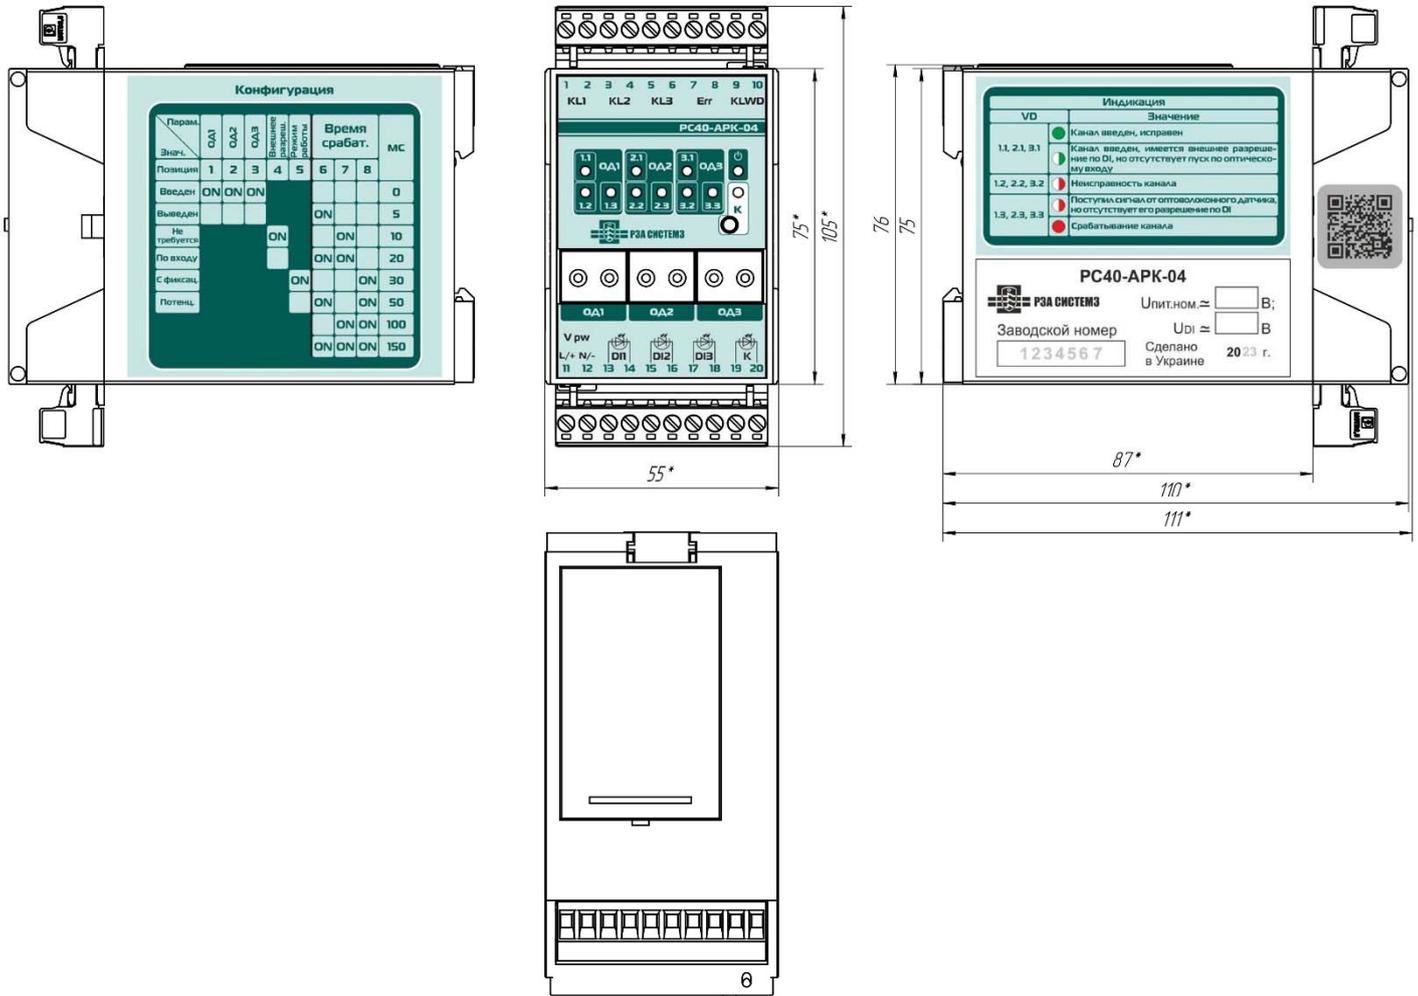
Габаритные и присоединительные размеры устройства РС40-АРК-04
